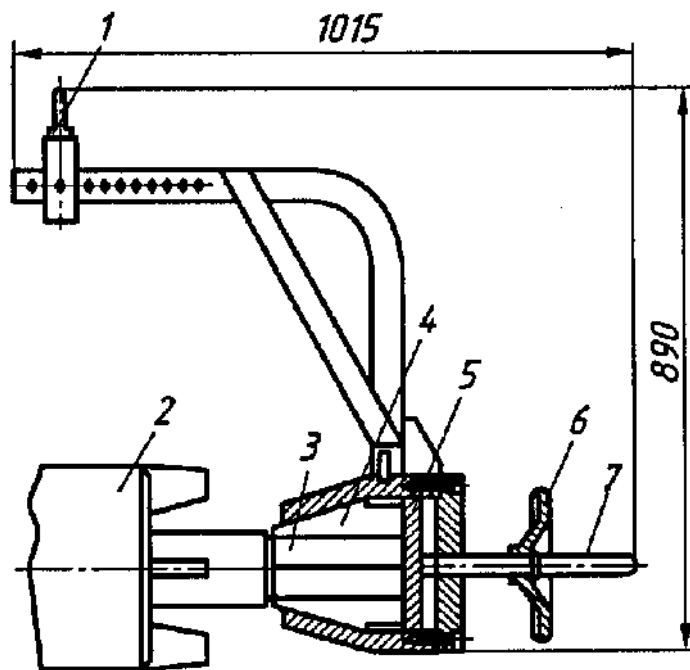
Схема конструкции приспособления для выема и ввода ротора электродвигателя: 1 – серьга; 2 – ротор; 3 – вал; 4 – кулачки; 5 – пластина; 6 – рукоятка; 7 – ось
